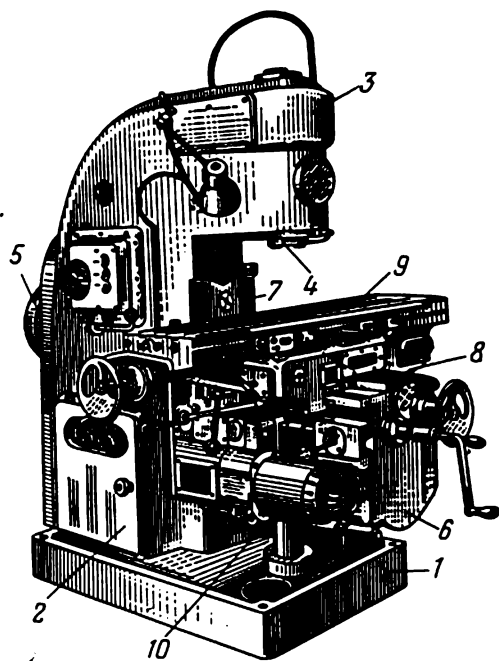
Vue d'ensemble de la fraiseuse verticale modèle 6H12
